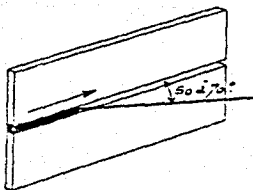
Soldadura horizontal en plano vertical
